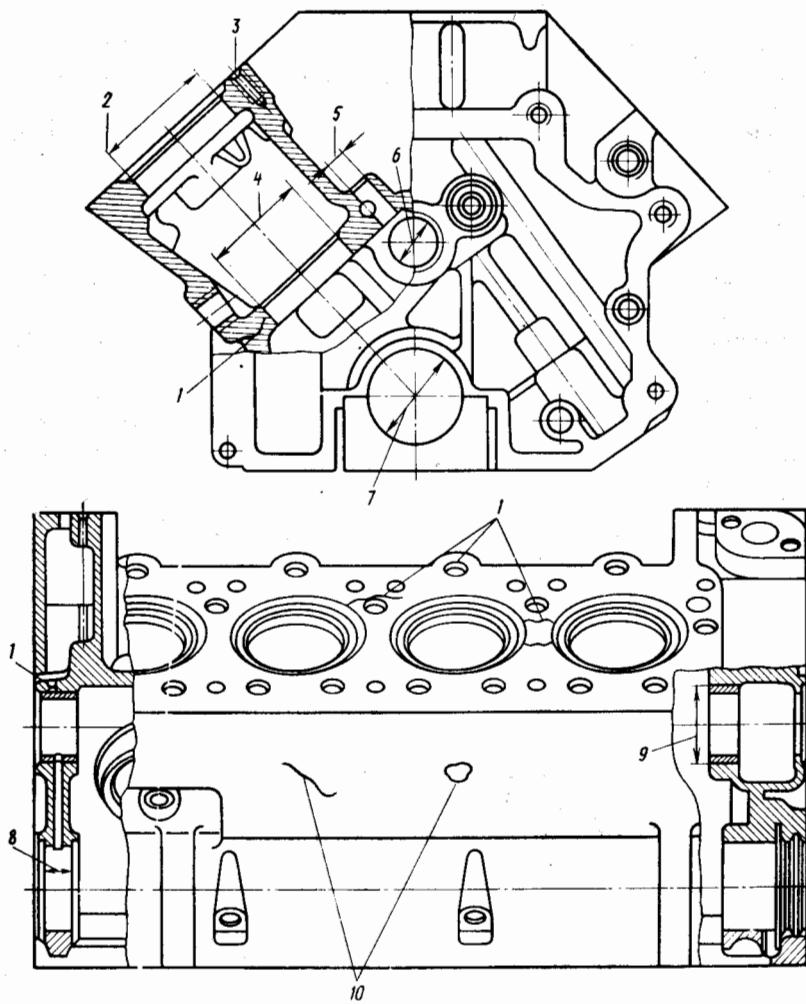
Основные дефекты блока цилиндров двигателя ЗИЛ-431410
